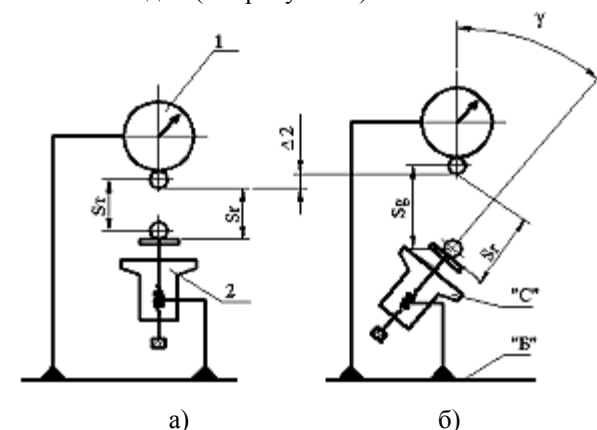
Кинематическая схема инструментальной наладки для поверки индикаторов: а) – теоретическое относительное положение поверяемого индикатора 1 и глубиномера 2; б) – действительное положение глубиномера и индикатора.
